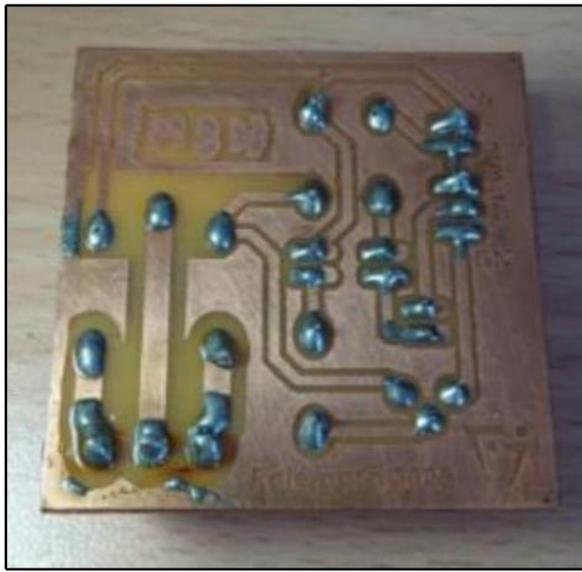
a: Relé optoacoplado GAX1- Soldadura
